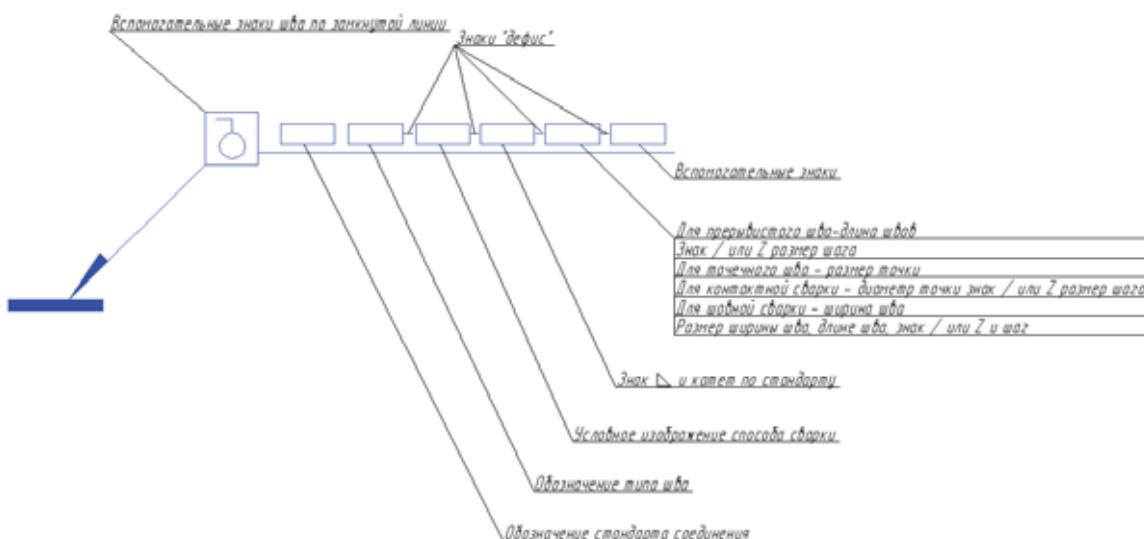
Структура условных обозначений сварных швов
